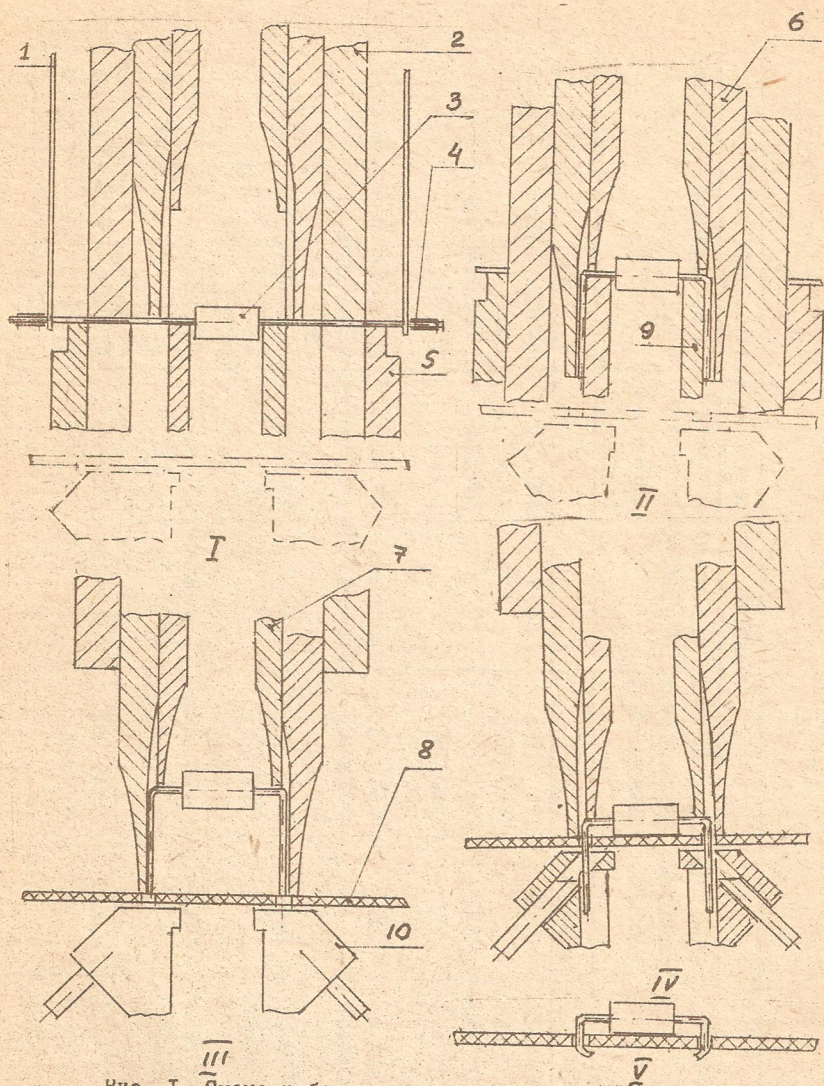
Схема работы укладочной головки: I - колесо периодической подачи ленты с ЭРЭ; 2 - пуансон обрезки выводов ЭРЭ; 3 - ЭРЭ, вклеенное в ленту; 4 - лента; 5 - матрица обрезки; 6 - пуансон гибки; 7 - толкатель устройства досылки ЭРЭ; 8 - плата; 9 - матрица гибки; 10 - нижняя подгибочная головка. Последовательность работы головки: I - вырезка ЭРЭ; II - гибка выводов ЭРЭ; III - заталкивание выводов ЭРЭ в монтажные отверстия платы; IV - подрезка и подгибка выводов ЭРЭ снизу; V - ЭРЭ установлен
